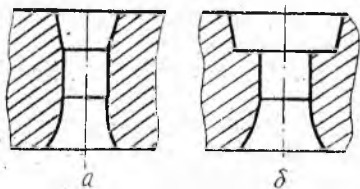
Различная конструкция канала матрицы: *a* — 8 прессовок, *б* — 23 прессовки
